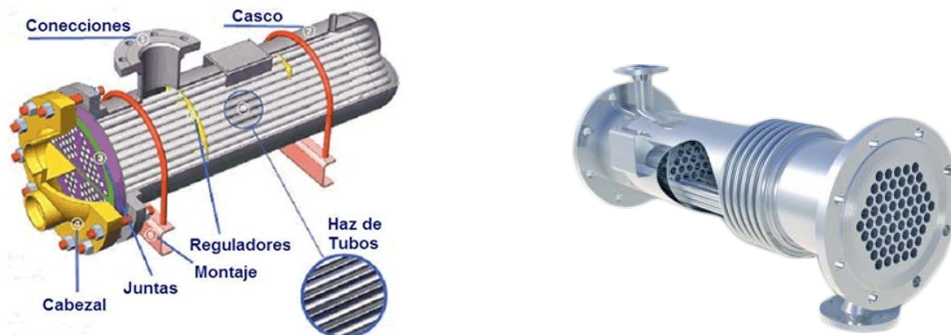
Evaporador de carcasa y tubo (<http://www.thermecs.co/>)
